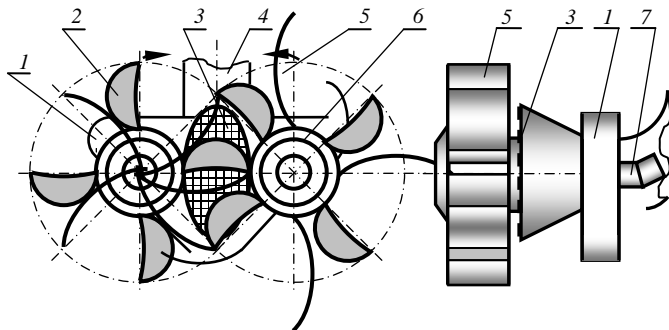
Схема двухроторного черпакового разрыхлителя: 1 – редуктор; 2 – черпаки; 3 – заборная сетка; 4 – всасывающая труба; 5 – очистители; 6 – ступицы; 7 – гидропривод
